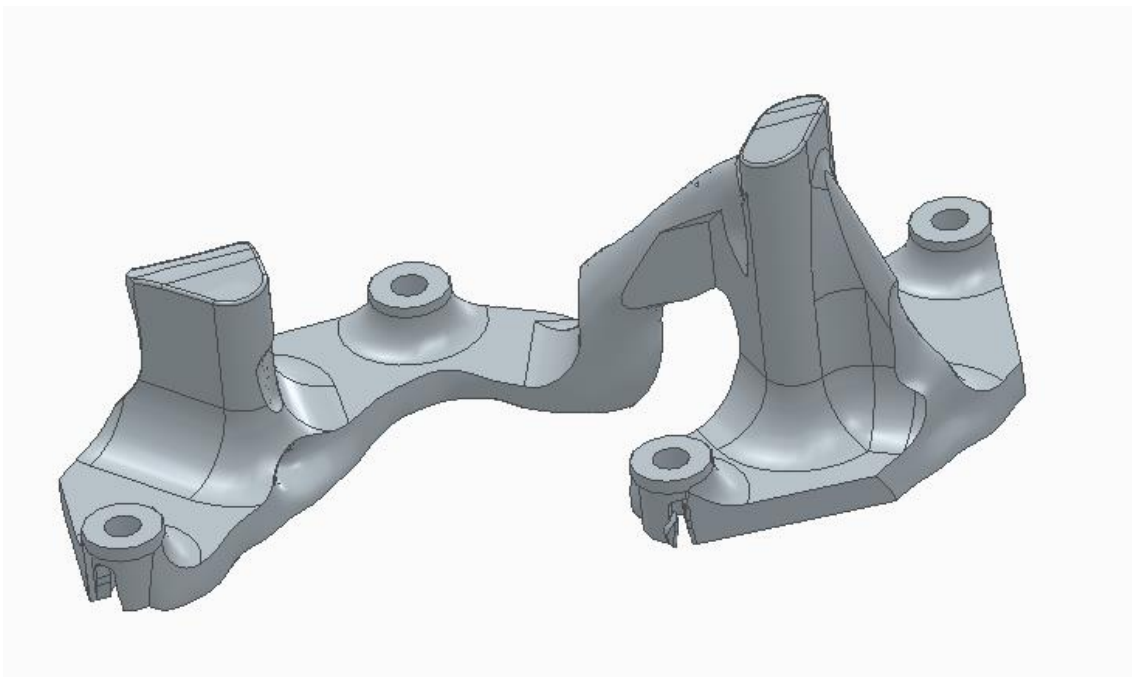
Optimización del módulo 2 del utillaje para pieza
